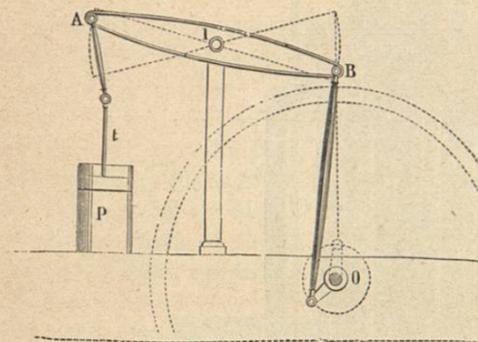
Principio de la transmisión en las máquinas de balancín
